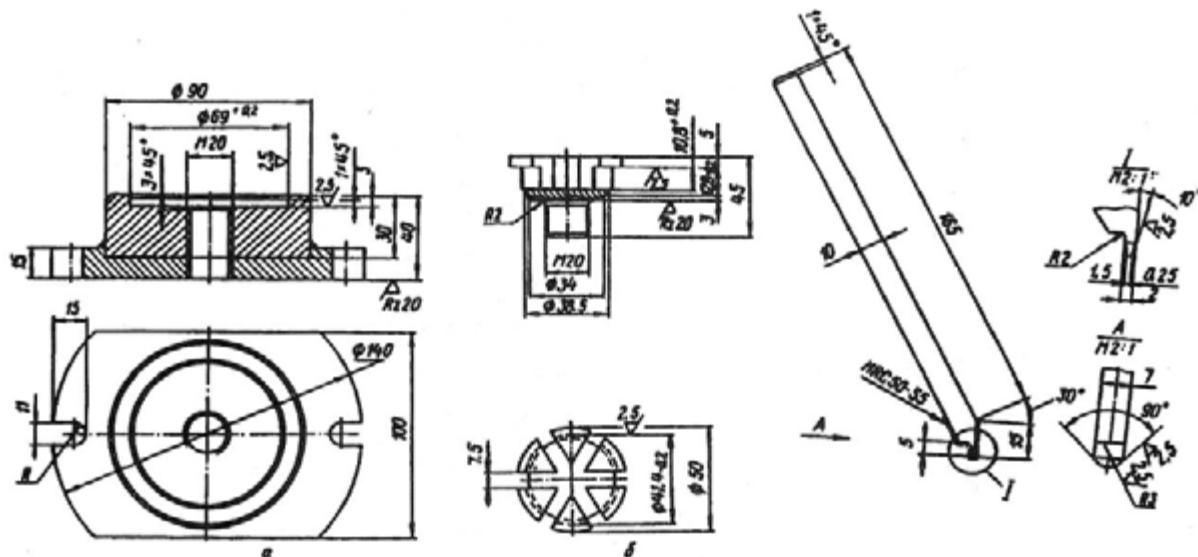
Детали ремонтного инструмента для монтажа опорной пяты:
